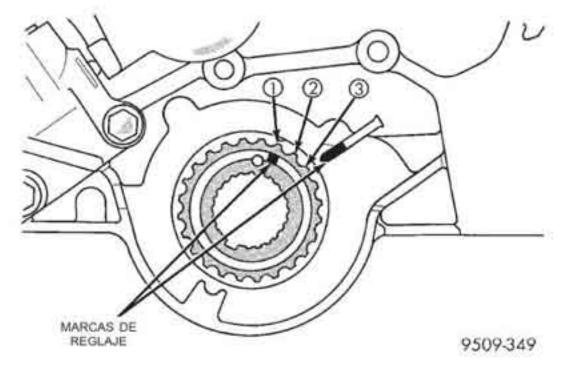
Sincronización de la rueda dentada del cigüeñal
